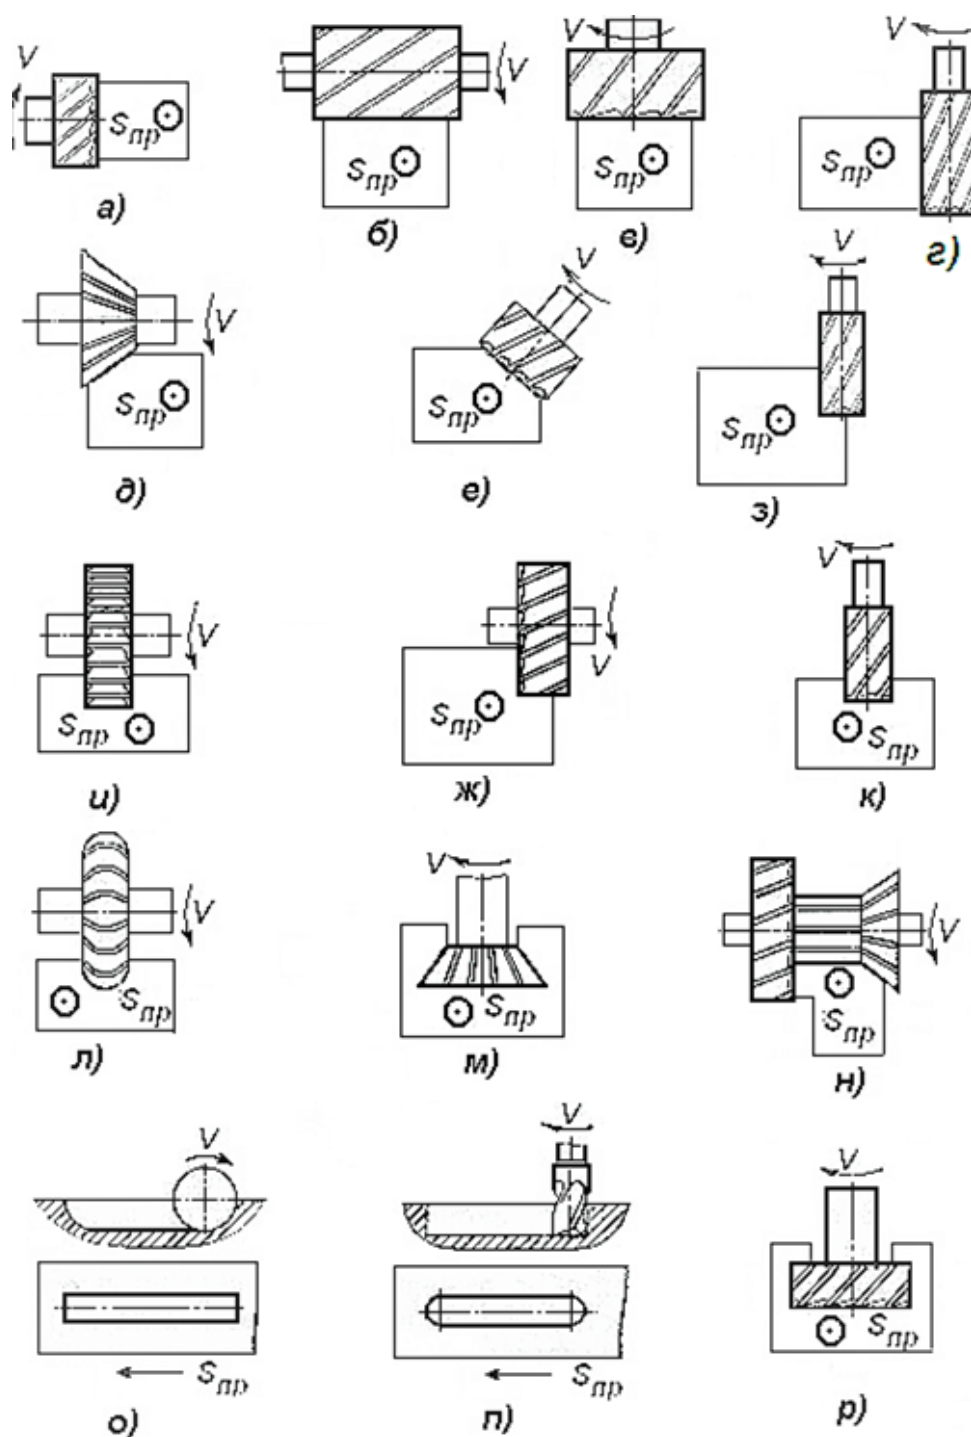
Типы фрез и схемы обработки поверхностей:
